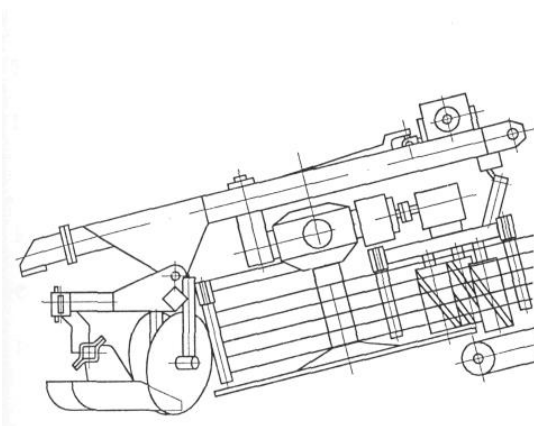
Двороторний очисник з вертикальним розташуванням валів і пасивними робочими органами
